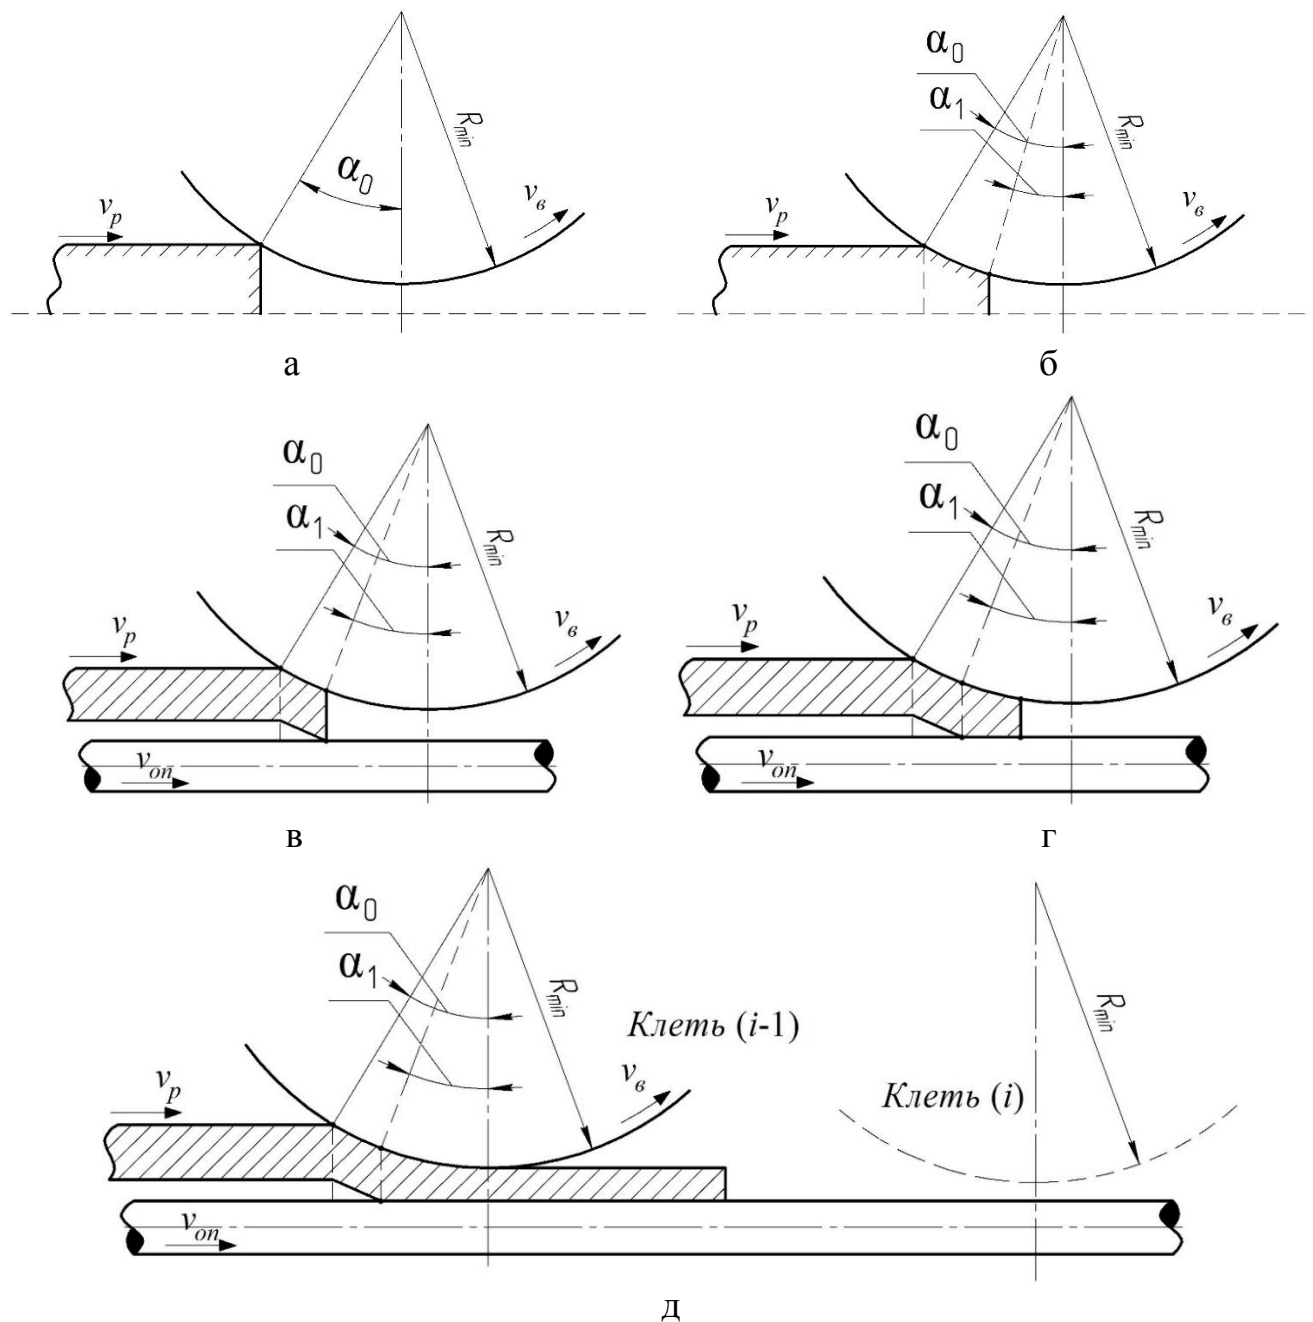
Стадии захвата металла валками в чистовых калибрах
